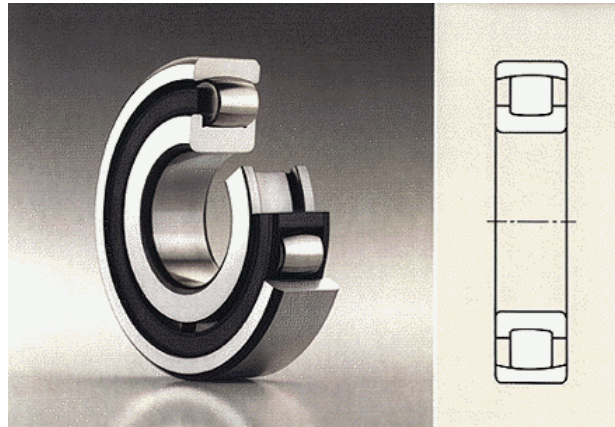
Rodamiento oscilante de rodillos de una sola hilera o rodamiento de rodillos esféricos
